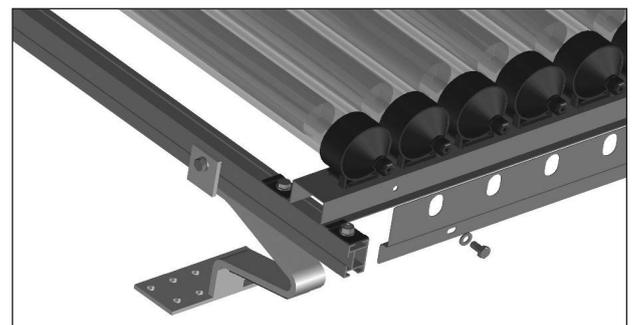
Montage de l'équerre en tôle sur la face inférieure du rail équerre.
